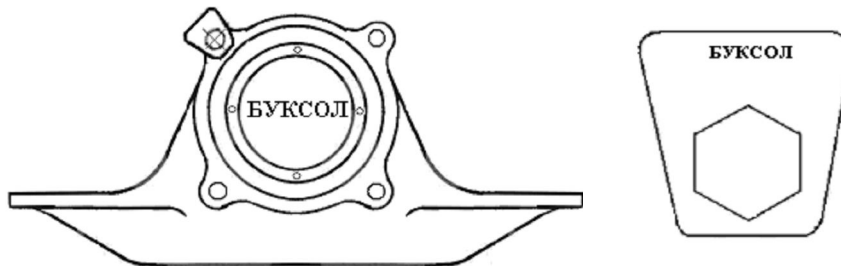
Отличительные признаки буксового узла с подшипниками роликовыми цилиндрическими, заправленными смазкой Буксол
